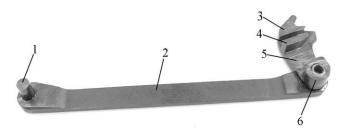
Спусковая тяга с рычагом взвода: 1 — цапфа; 2 — спусковая тяга; 3 — разобщающий выступ; 4 — выступ самовзвода; 5 — рычаг взвода; 6 — пяточка рычага взвода
